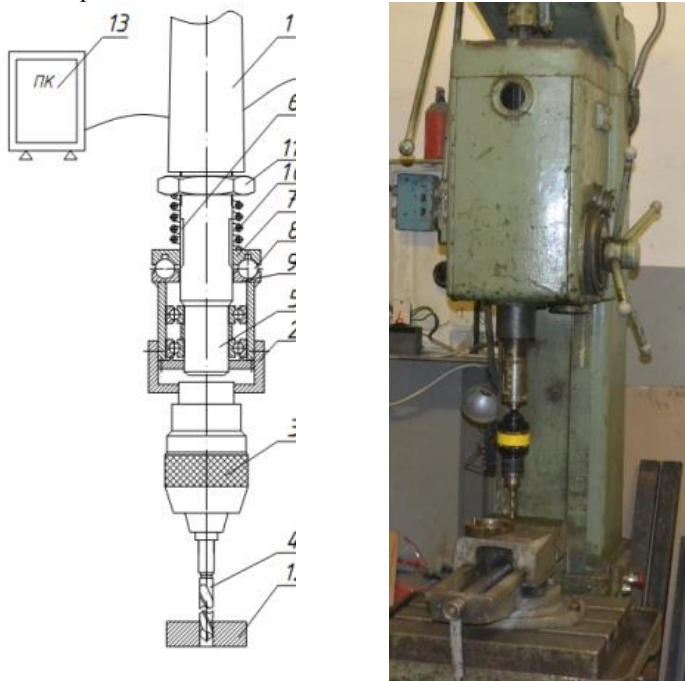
Конструкція пристрою для дослідження стійкості свердла-мітчика: а) конструктивна схема; б) загальний вигляд
